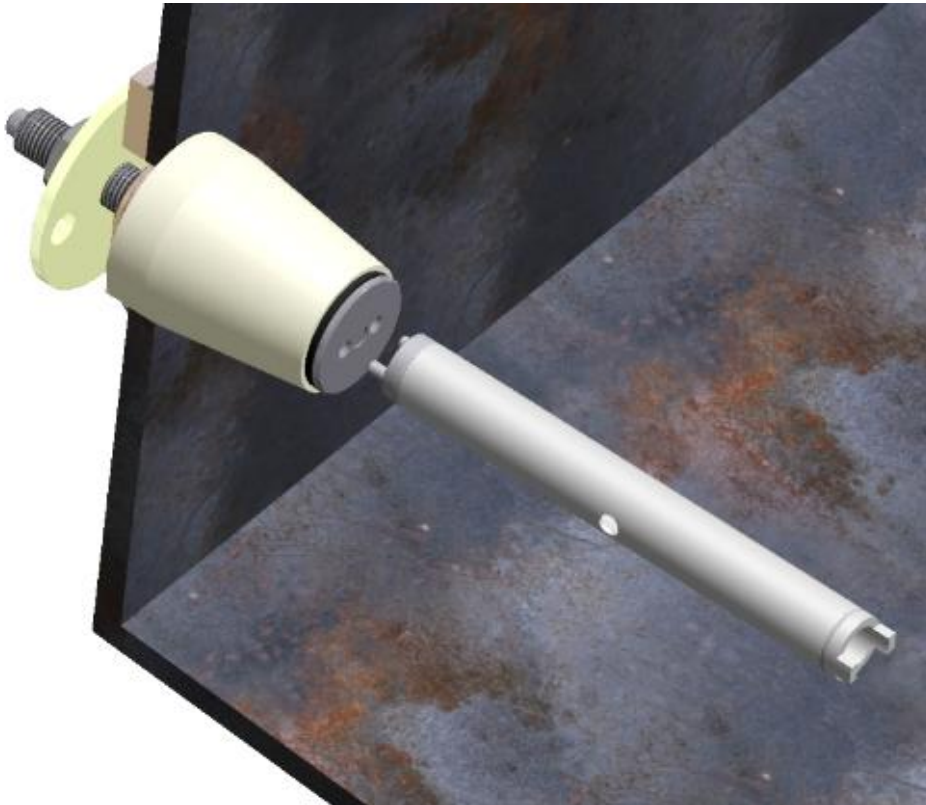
Mit dem Einstellwerkzeug können Sie alternativ das Einbettwerkzeug von der Innenseite des Verteilers öffnen und schließen.
